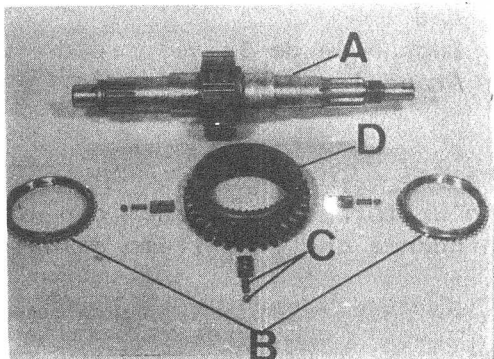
Conjunto eje principal y sincronizador de 1a y 2a V.
